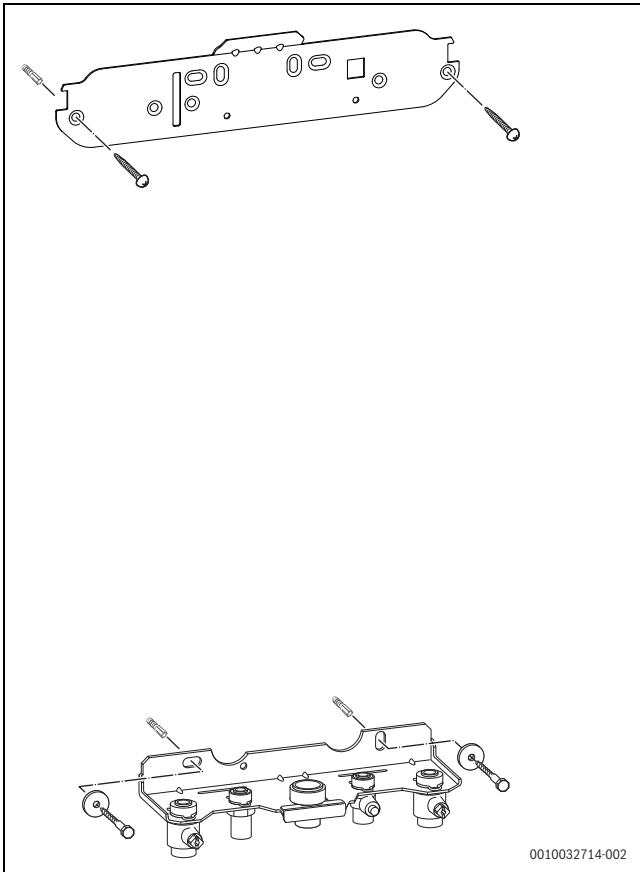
Montage de la plaque de fixation et de la plaque de montage pour le raccordement
